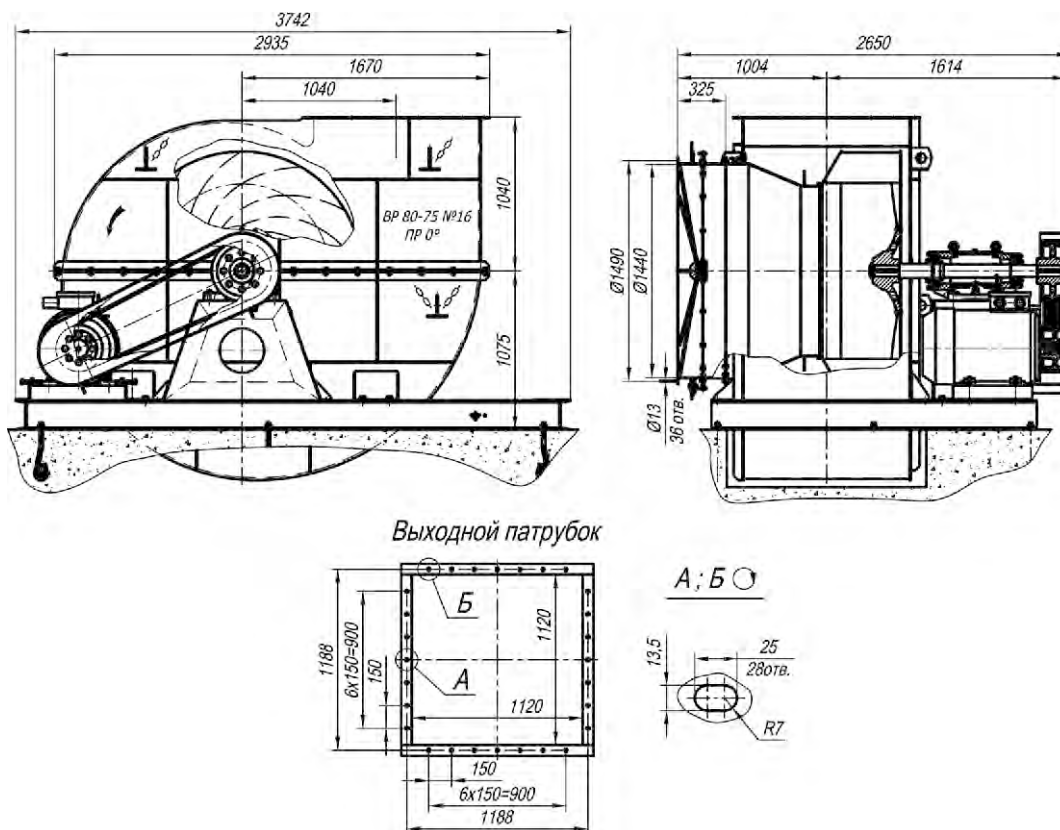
Габаритные и присоединительные размеры вентилятора ВЦ 4-70 (80-75) № 16 исп-5.
